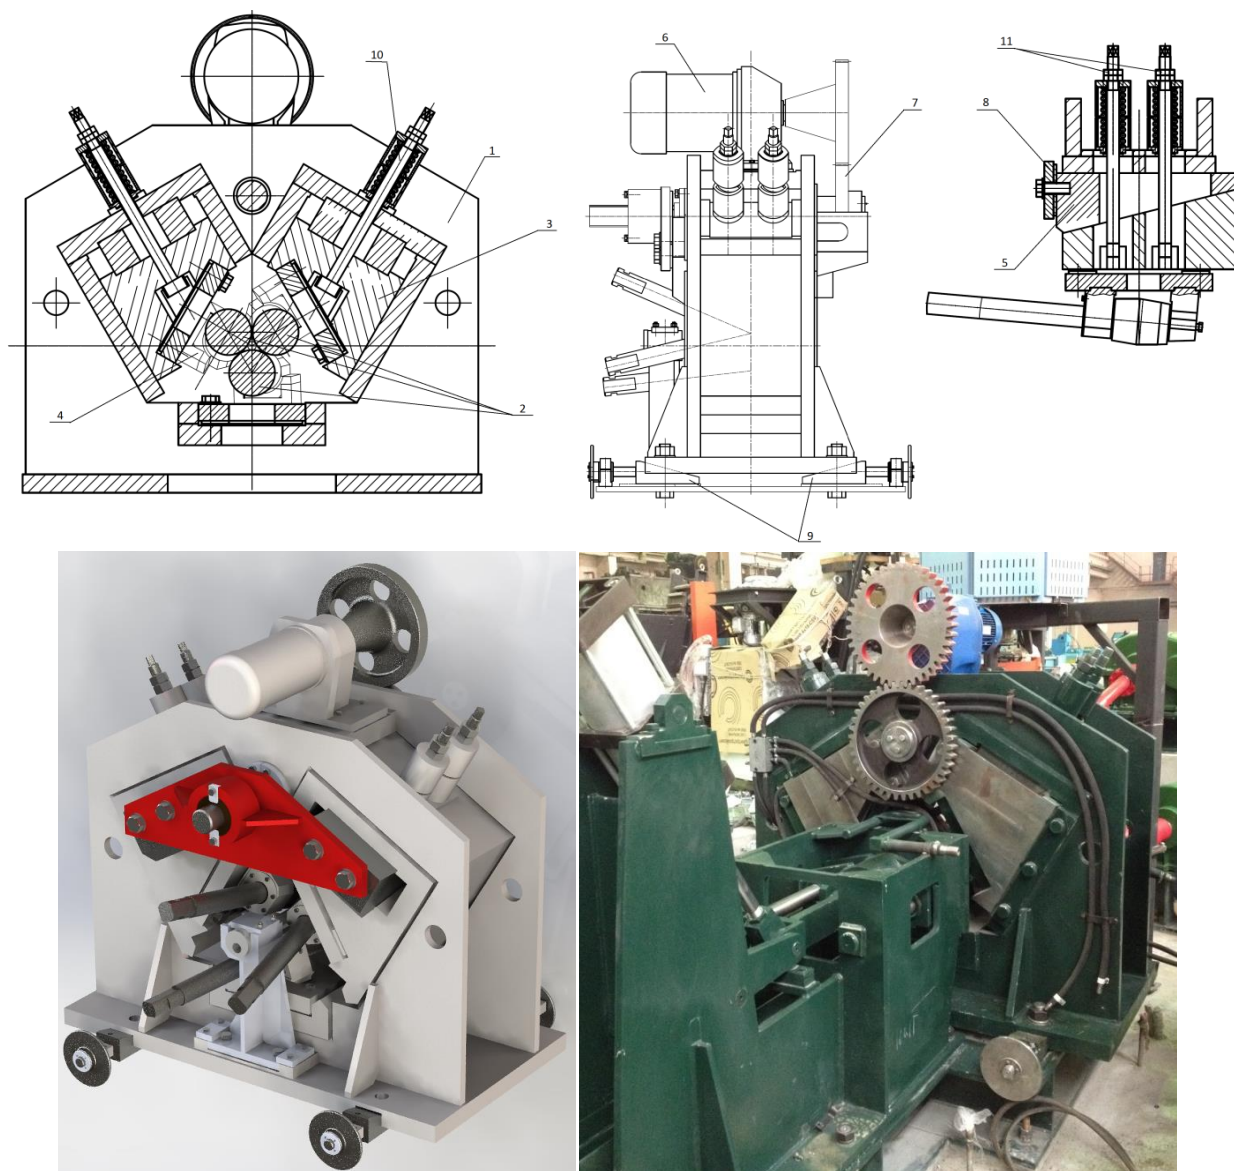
Рабочая клеть трехвалкового стана винтовой прокатки: 1 – станина; 2 – рабочие валки; 3 – кассета; 4 – подушка валка; 5 – клин; 6 – мотор-редуктор; 7 – зубчатое зацепление; 8 – траверза; 9 – клинья; 10 – тяга; 11 – затяжные гайки
